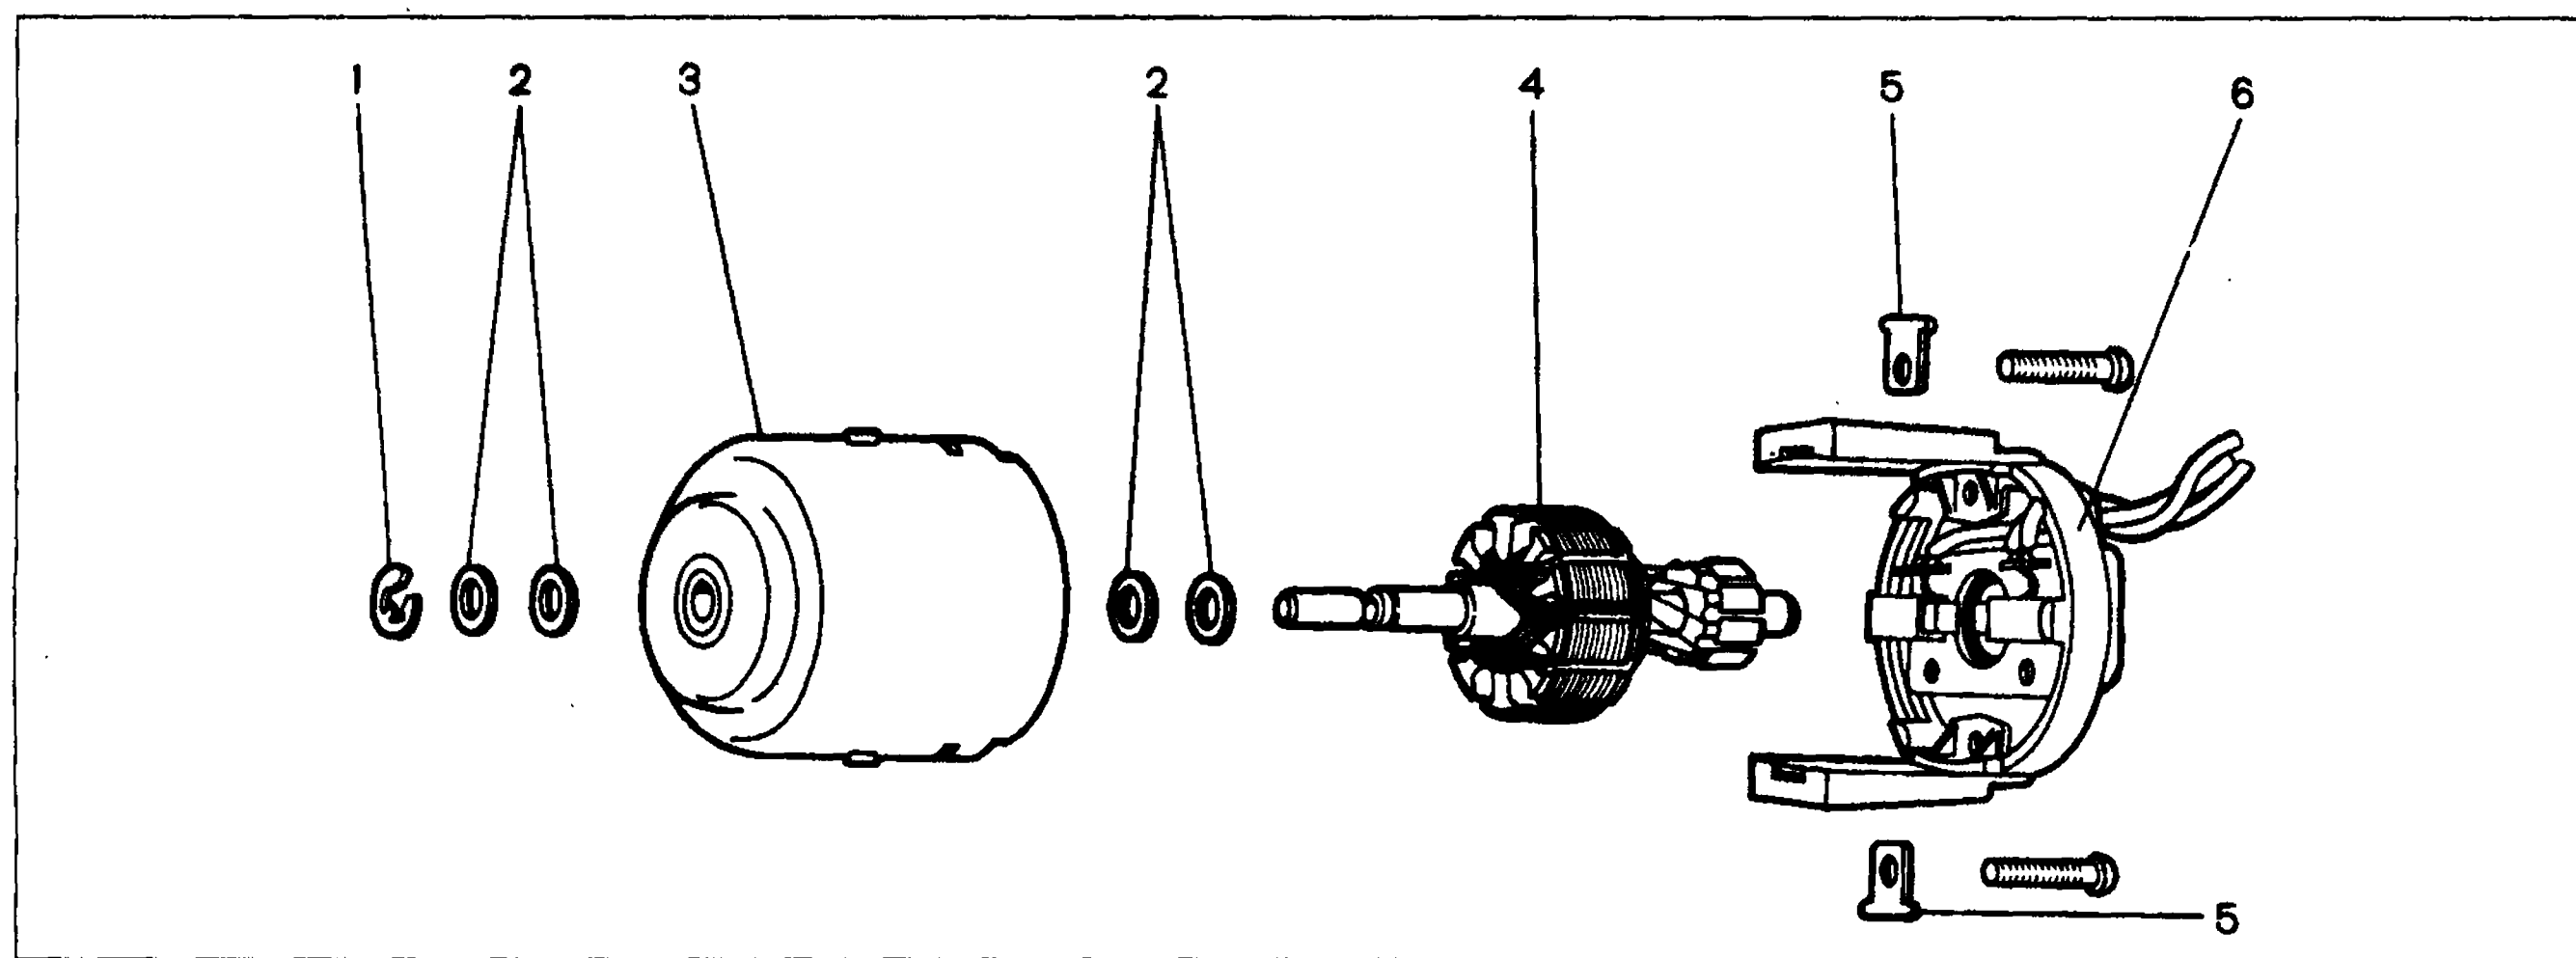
Детали электродвигателя отопителя: 1-стопорная шайба; 2-шайбы; 3-корпус; 4-якорь; 5-сухари; 6-крышка
